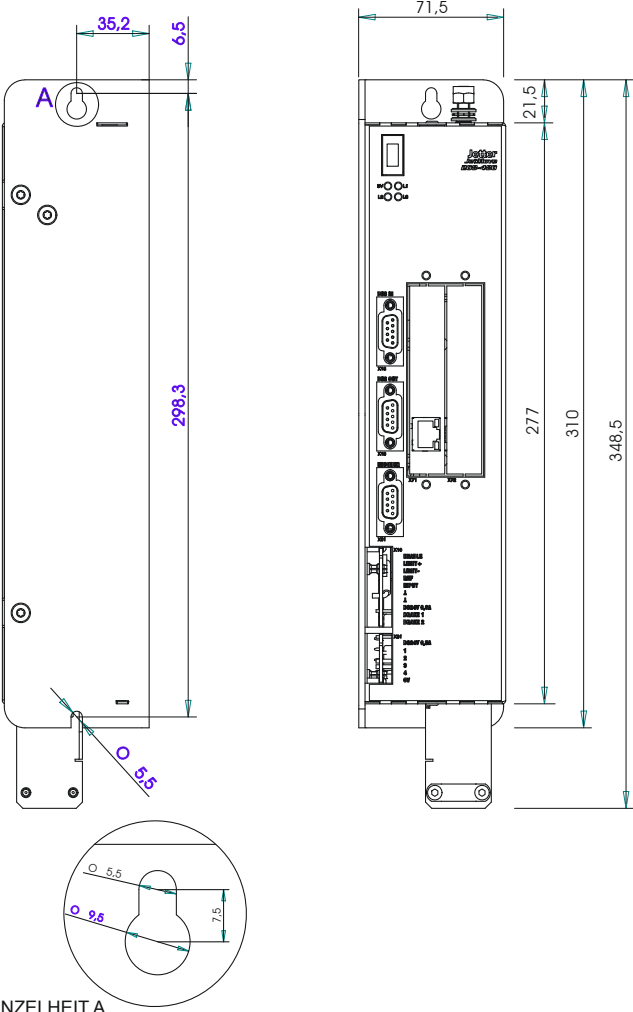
Rück- und Frontansicht des Gehäuses des JetMove 204-480 mit Bohrungen
